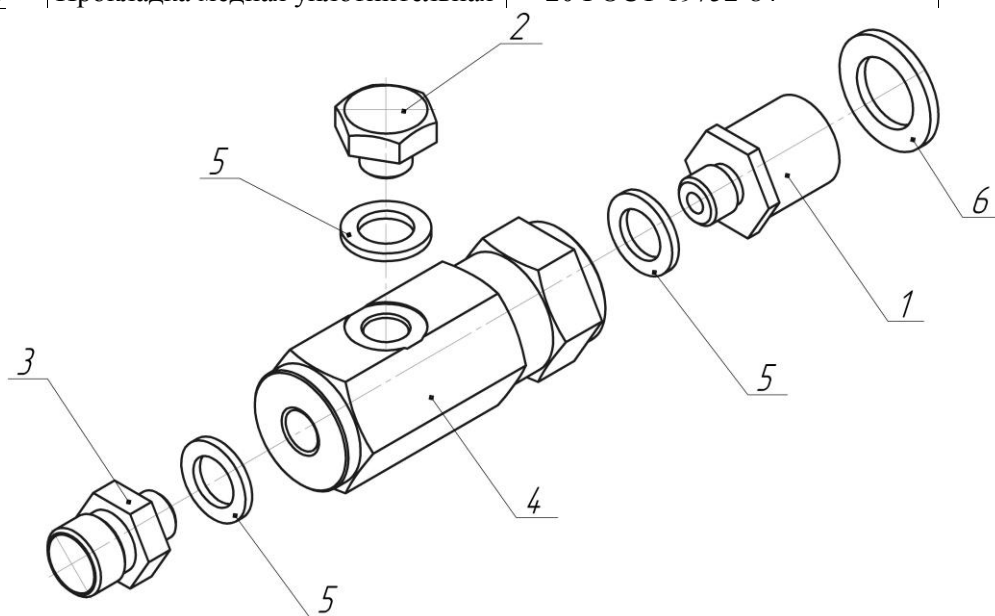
Клапан обратный в сборе ИЯПБ.27.06.11.000
